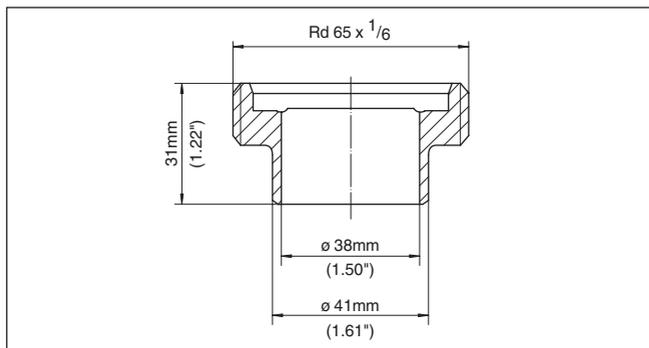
Medidas da luva para soldagem união rosçada para tubo DN 40
